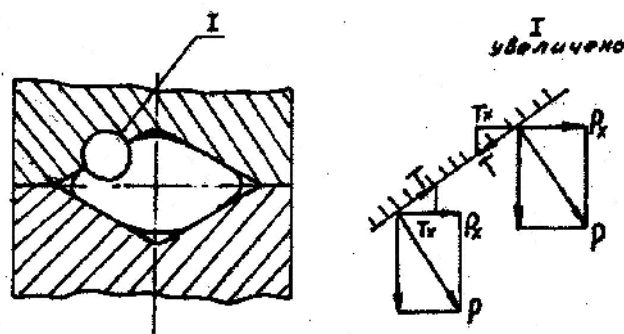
Схема течения металла при протяжке круглых заготовок в вырезных бойках.
